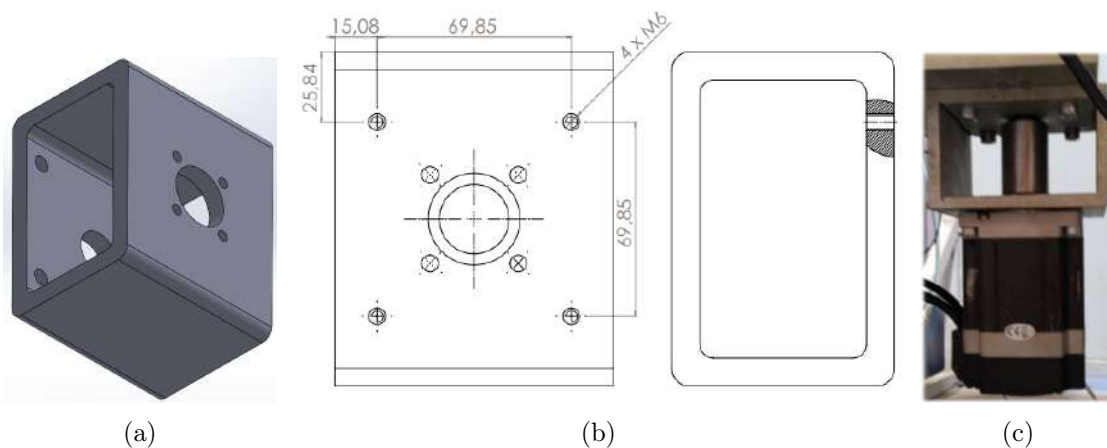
Fixação do motor na máquina: (a) Suporte inicial, (b) Desenho das alterações efetuadas, (c) Aplicação do motor e acoplamento na máquina.
